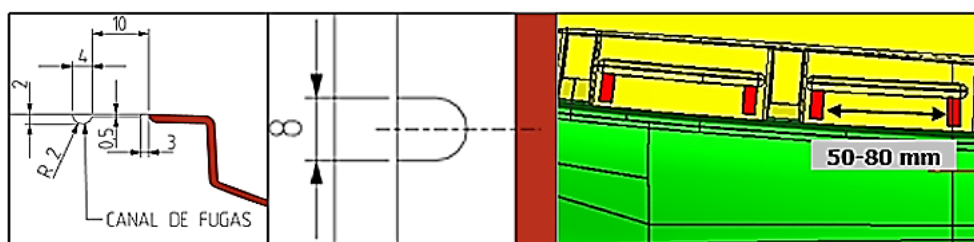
Canal de fugas em moldes para trabalhar em máquinas de injeção < 350 T (Grupo Simoldes, 2016)
